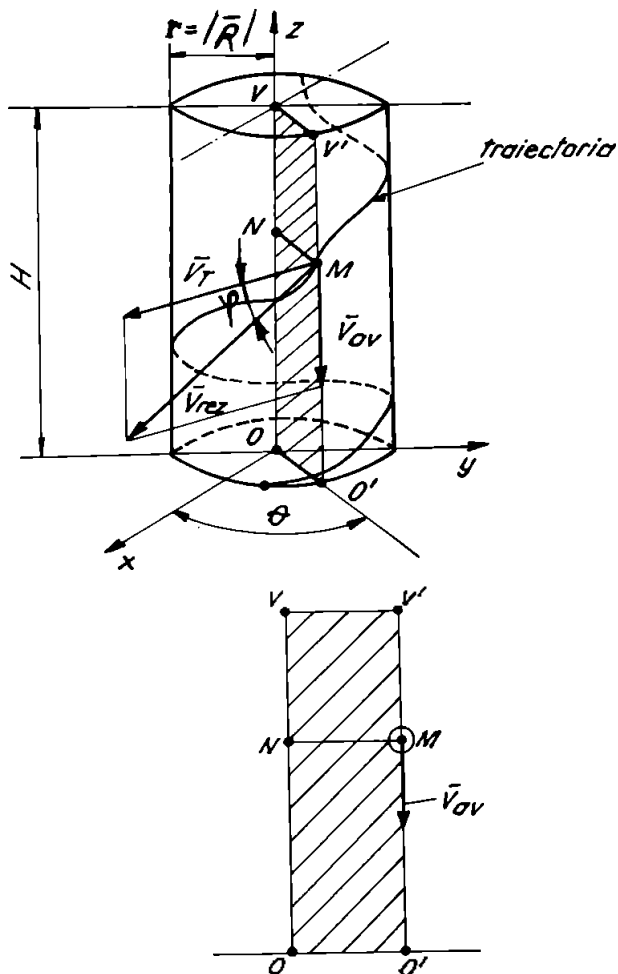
Figură explicativă pentru studiul cinematicii prelucrării prin EE cu TM a E sculă masiv pe suprafață cilindrică.
